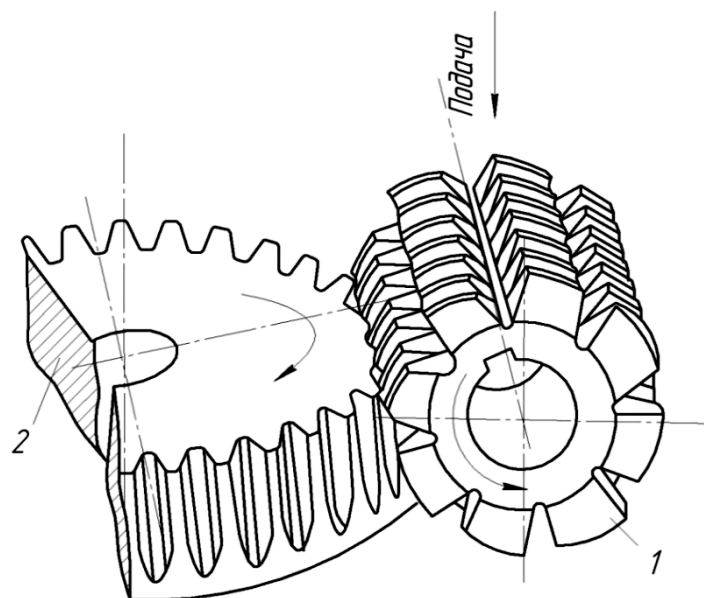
Схема нарізування зубів черв'ячною модульною фрезою:
